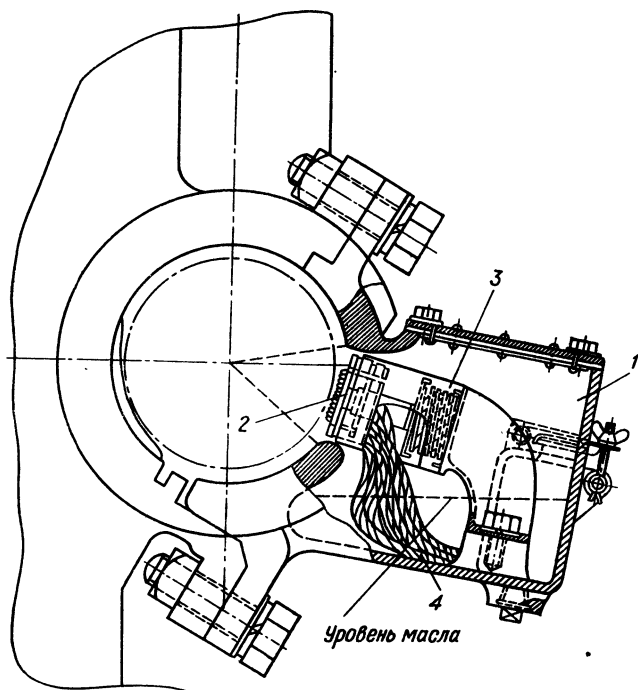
Польстерное смазочное устройство моторно-осевого подшипника
